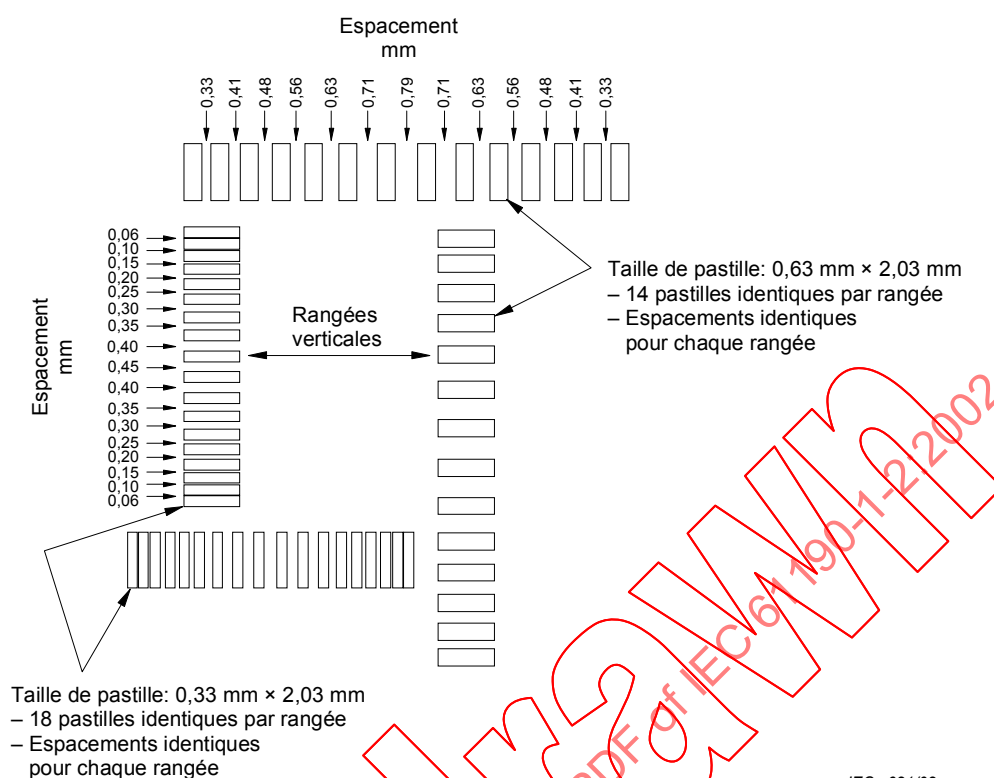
Epaisseur du pochoir de l'essai de glissement – 0,20 mm
